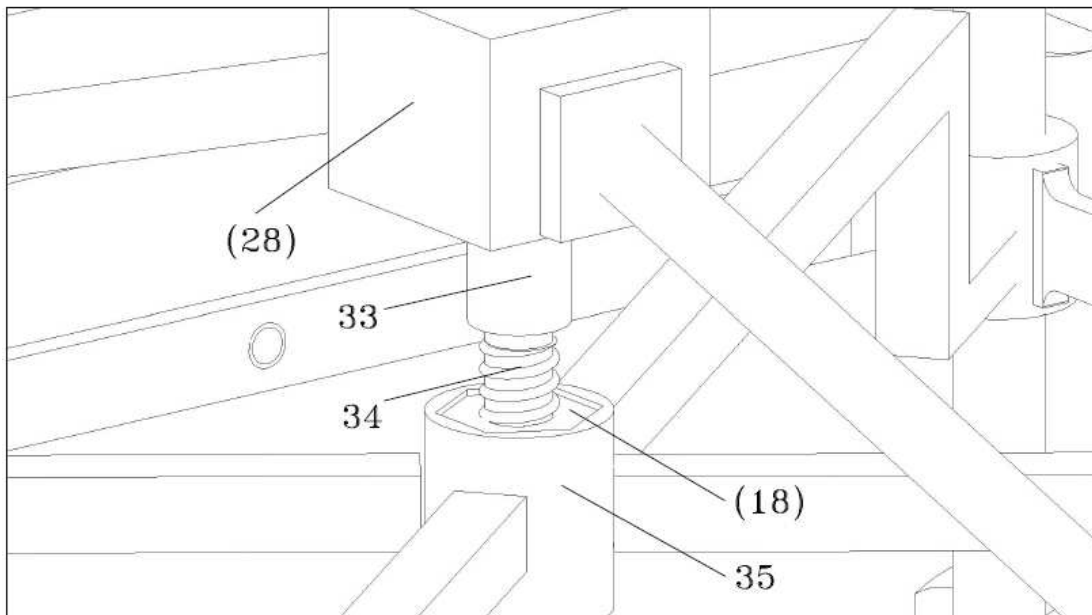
Esquema de Transmisión Motor – Tornillo-Tuerca.
